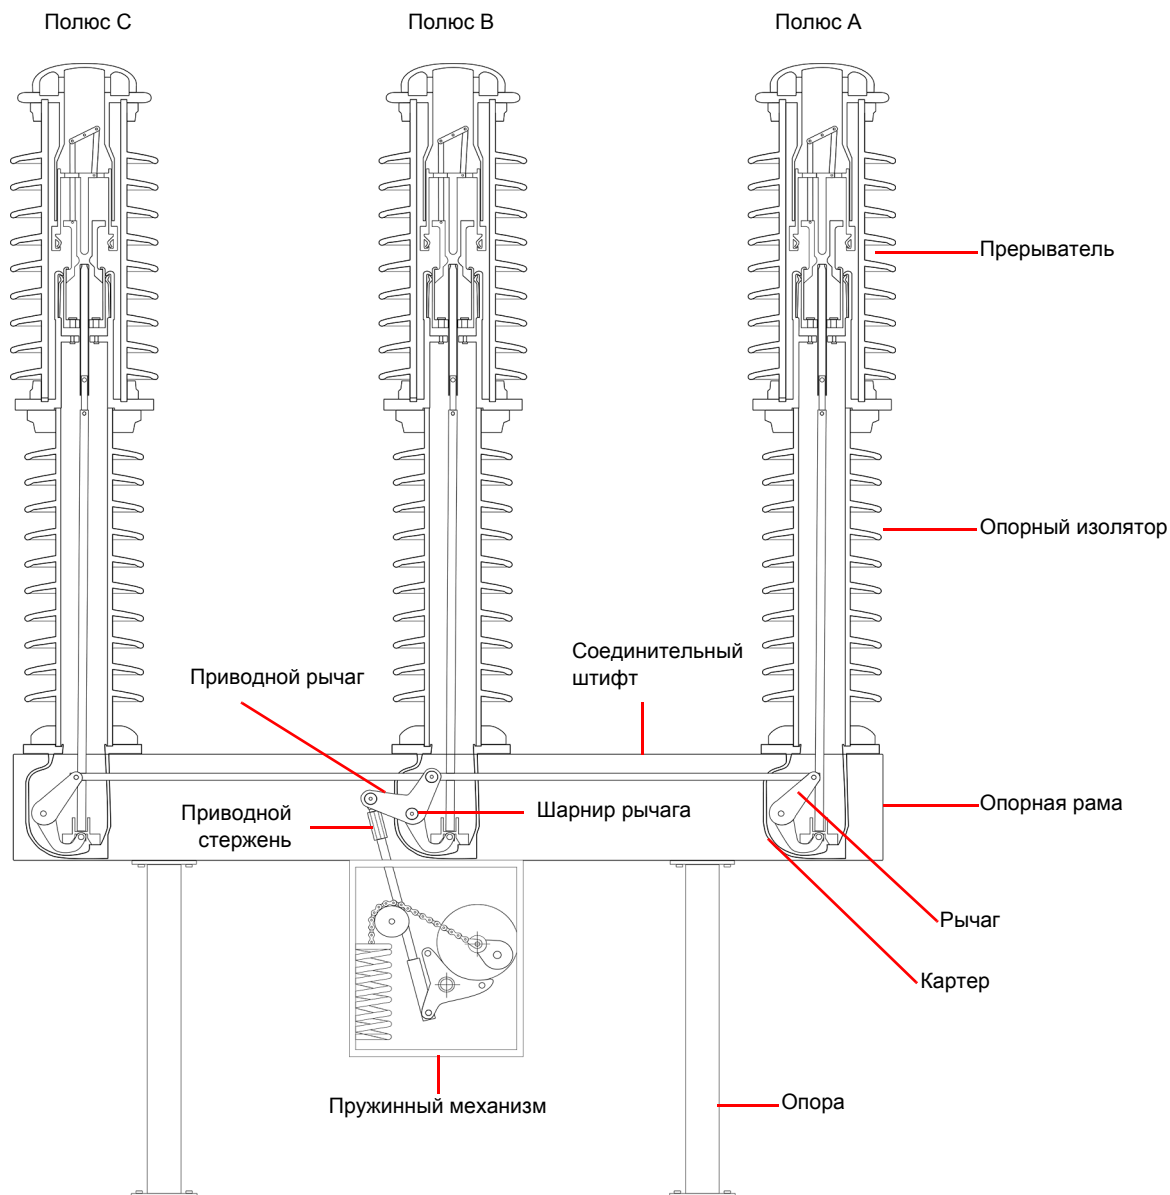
Пружинный колонковый высоковольтный выключатель
